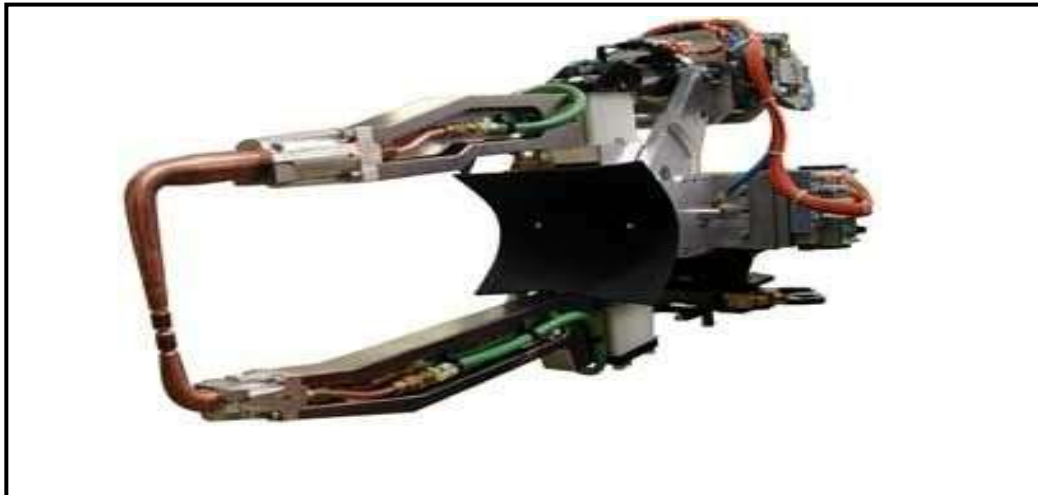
pince universelle de robot soudage par point.
